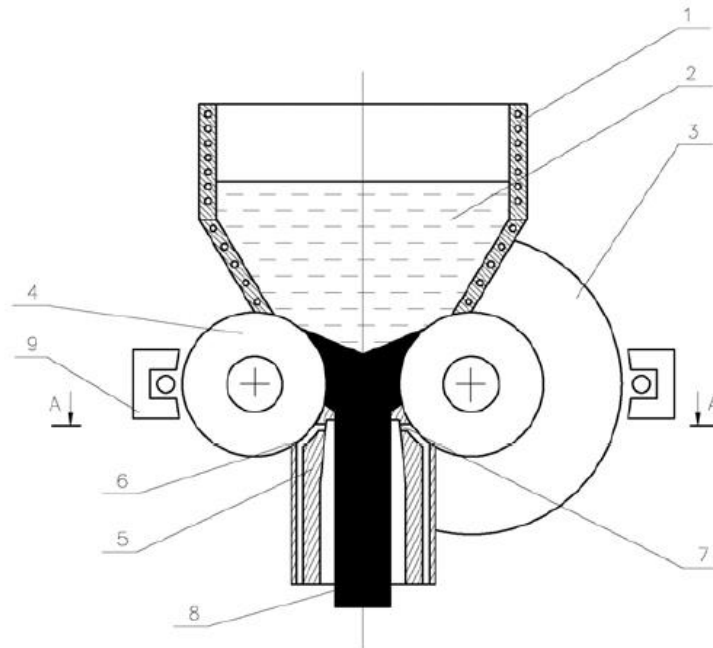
Схема процесса совмещенного процесса литья, прокатки и прессования: 1 - печь-миксер; 2 – расплав; 3 - валок с ручьем; 4 - валок с выступом; 5 - матрица; 6 и 7 - каналы для охлаждения матрицы; 8 - пресс-изделие; 9 – индуктор
